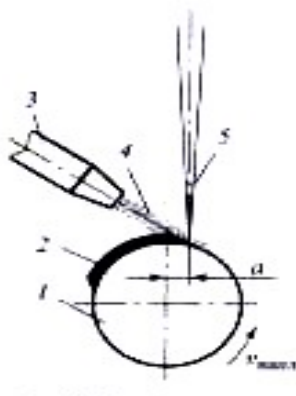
Схема процесса наплавки тел вращения: 1 – деталь, 2 – наплавленный валик, 3- транспортирующая трубка, 4 –наплавочный порошок, 5- лазерный луч.
